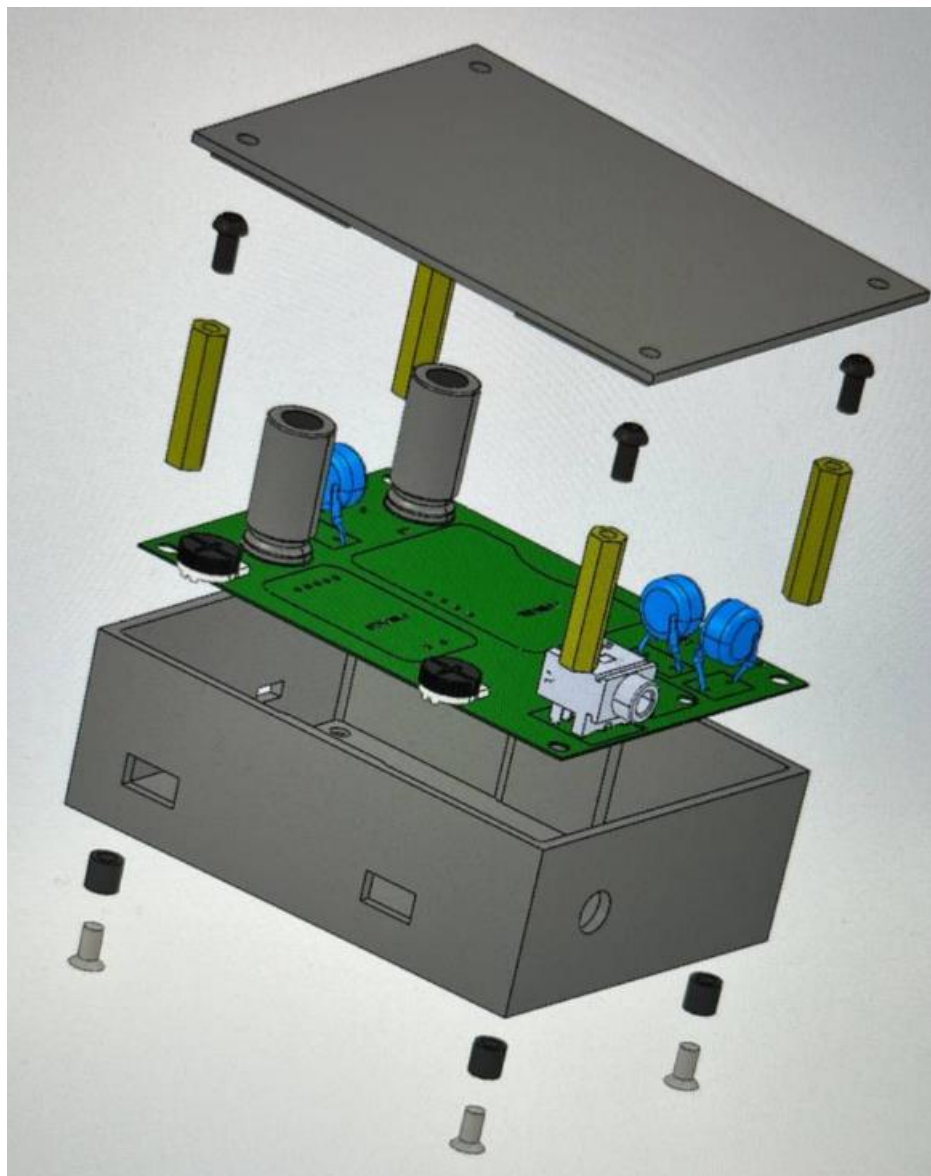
Конструкція деталей корпусу слухового апарату
